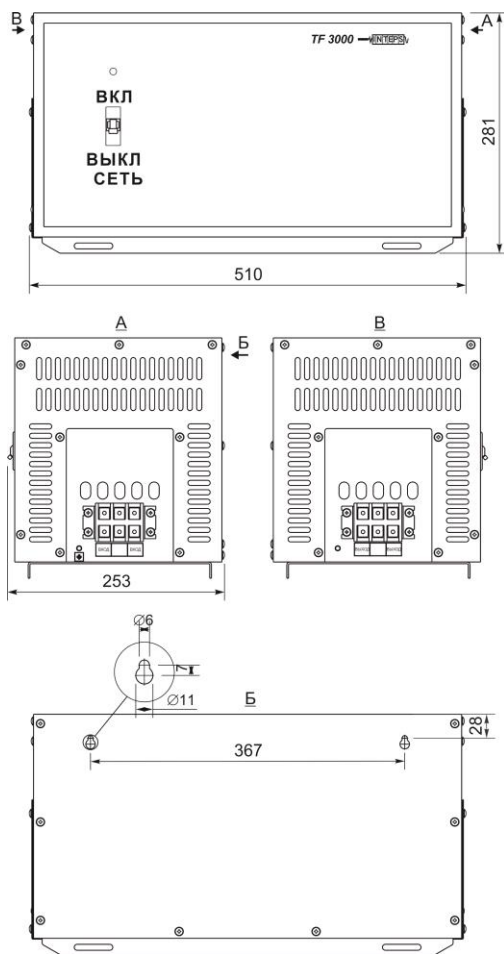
Габаритные и установочные размеры трансфильтров LIDER: TF500, TF1000, TF1500, TF2000, TF3000
